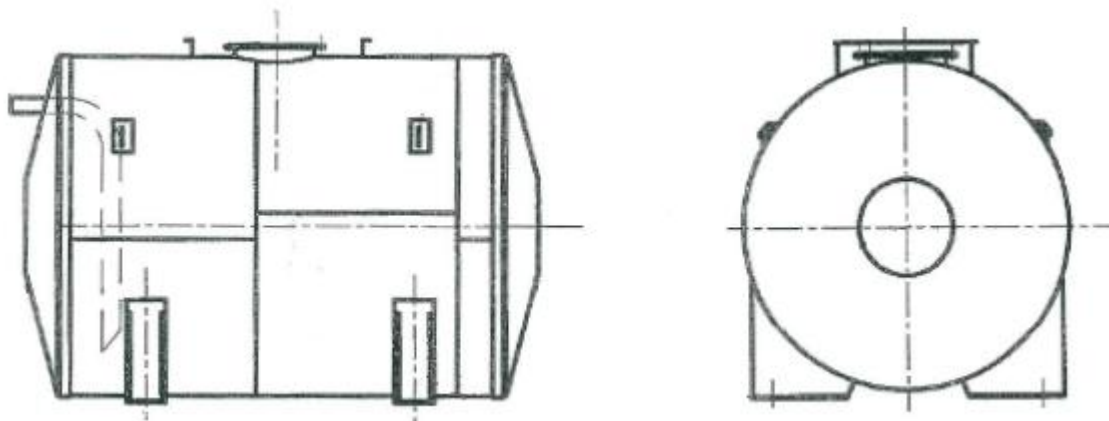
Общий вид эскиза резервуара РГС-10
